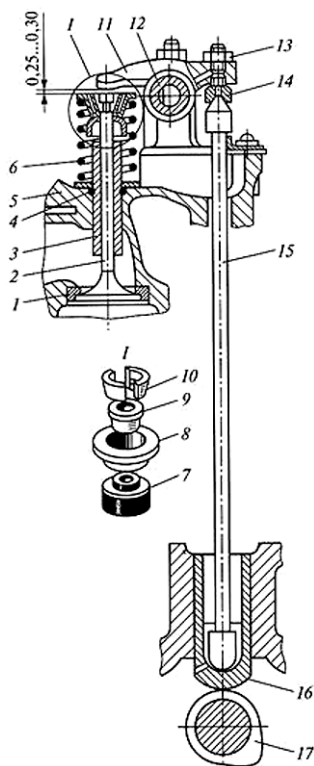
Схема газораспределительного механизма с верхним расположением клапанов: 1 – седло; 2 – клапан; 3 – направляющая втулка; 4 – стопорное кольцо; 5 – головка цилиндров; 6 – пружина; 7 – уплотнительный колпачок; 8 – тарелка; 9 – втулка; 10 – сухарики; 11 – коромысло; 12 – ось; 13 – контргайка; 14 – регулировочный винт; 15 – штанга; 16 – толкатель; 17 – кулачок
